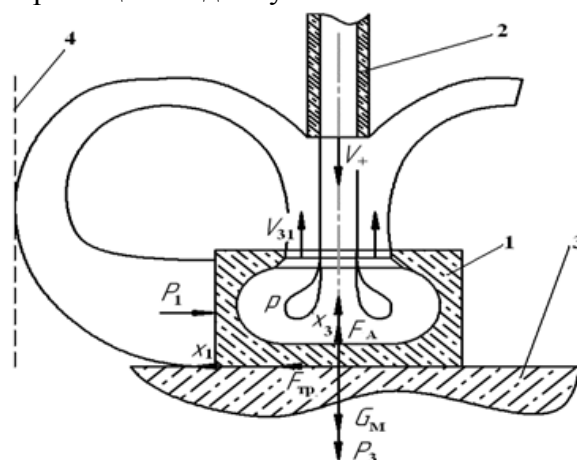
Компоновка металлоприёмника в промежуточном ковше и схема нагрузок: 1 – металлоприёмник; 2 – приемная труба; 3 – дно ПК; 4 – торец боковой перегородки ПК
